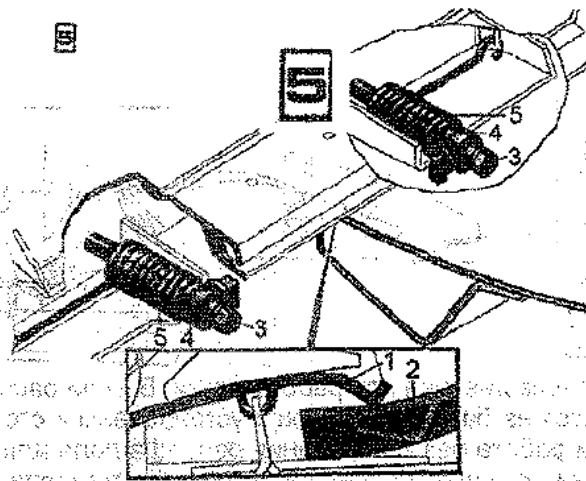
Схема переходного щитка: 1 – переходной уплотнительный щиток; 2 – днище проставки; 3 – болт; 4 – рифленый зацеп; 5 – пружина
